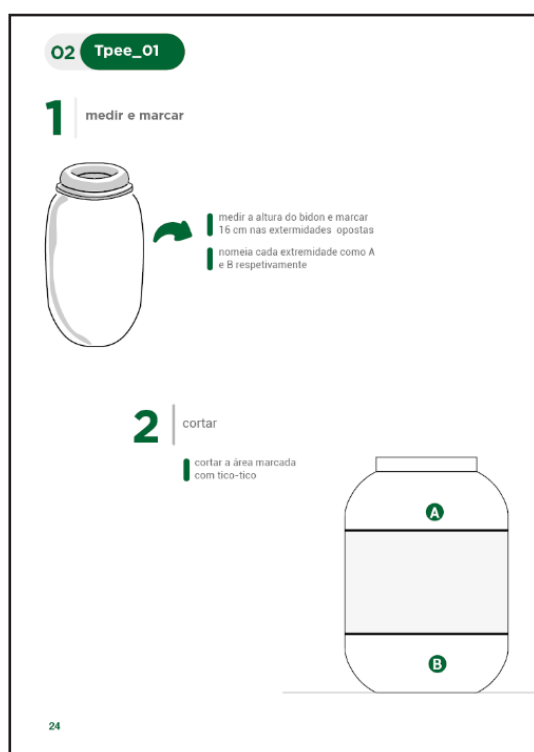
Guia de construção Tpee_01, antes da alteração (Autor 2020)
